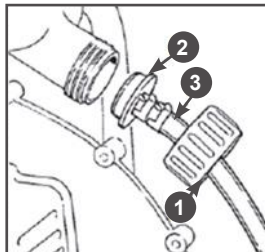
Демонтаж выпускного шланга опрыскивателя
